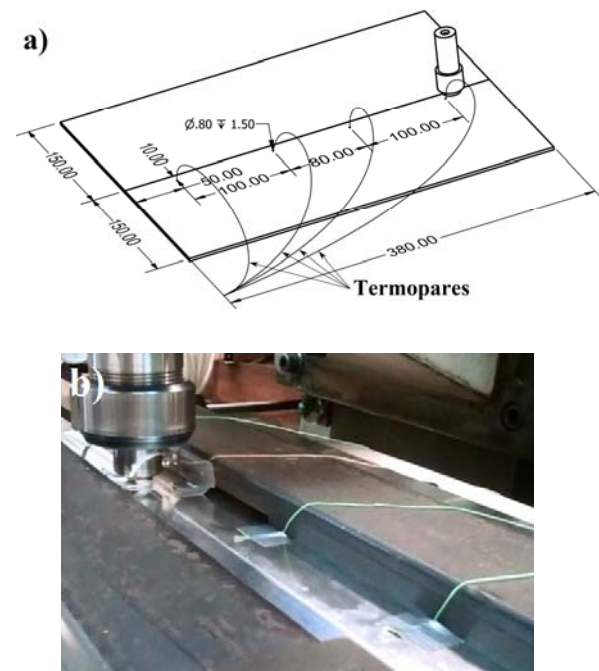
Configuração aplicada durante a soldadura: a) esquema de soldadura e localização dos termopares; b) imagem de uma soldadura.
